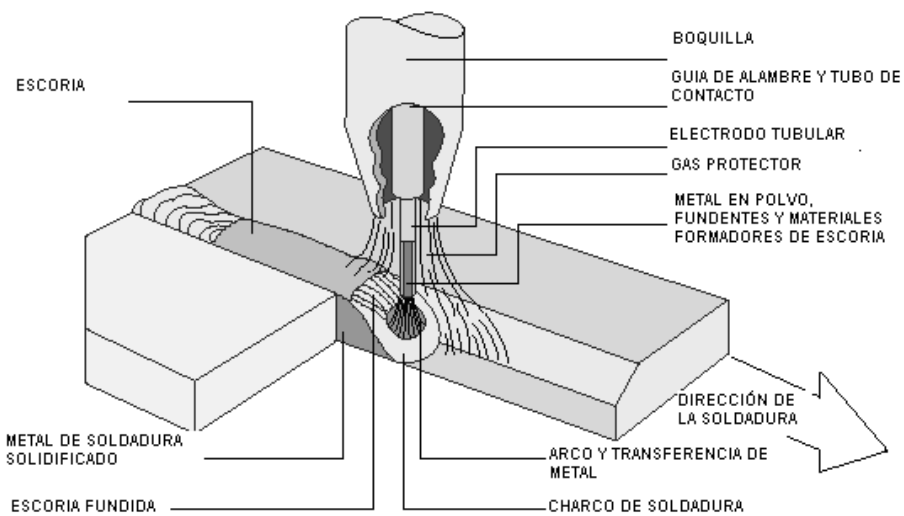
Soldadura por arco con núcleo de fundente protegido con gas
